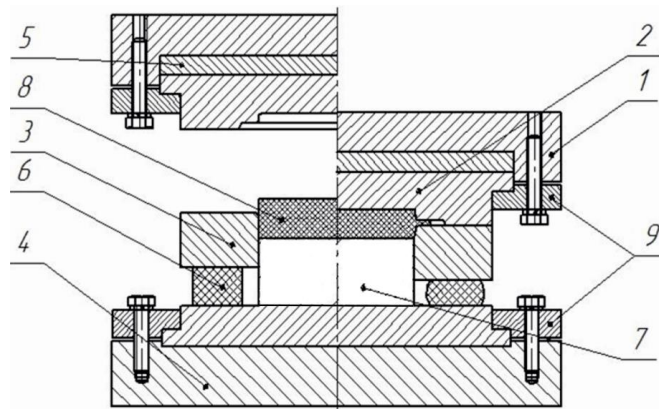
Конструктивна схема штаму для гарячого штампування пористих заготовок:
